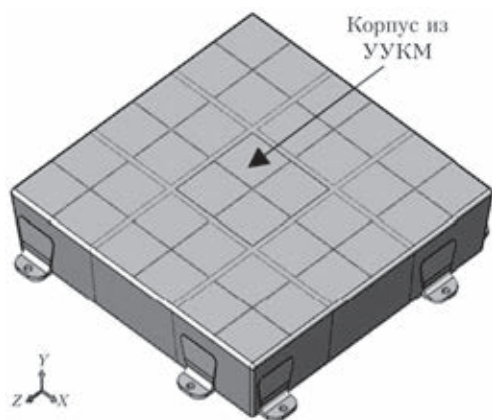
Конструкция теплозащитной плитки с корпусом из УУКМ или керамики
